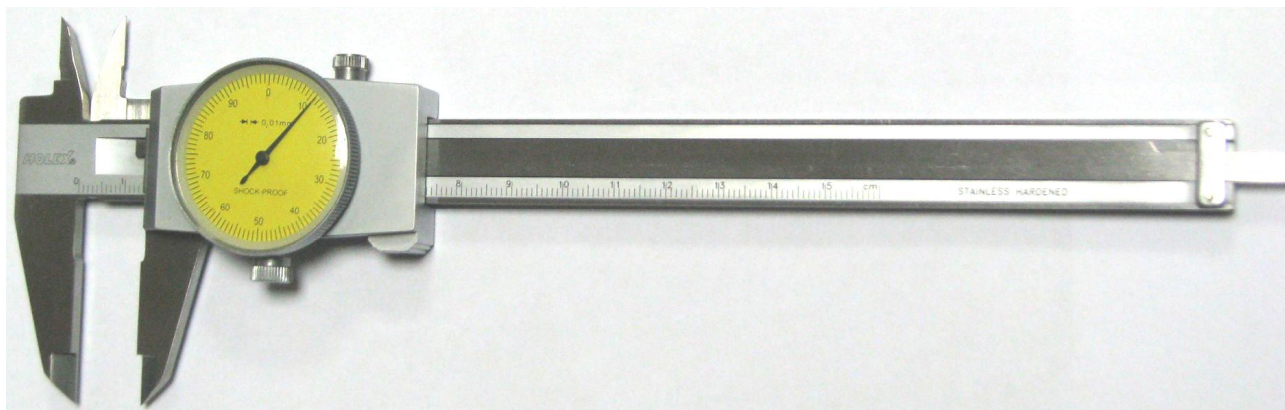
Внешний вид штангенциркуля Nolex с круговой шкалой
